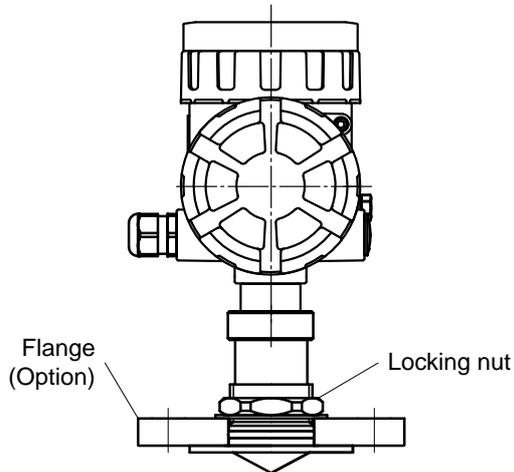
Fissaggio testa del trasmettitore
